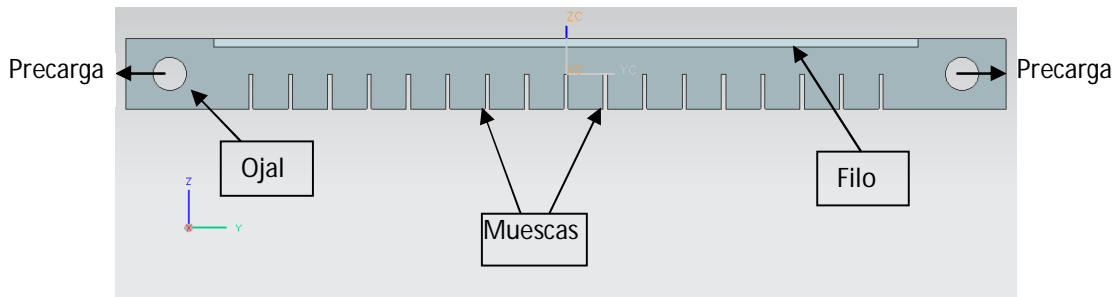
Cuchilla de corte horizontal con ranuras troqueladas o manufacturadas con piedra de desbaste.
